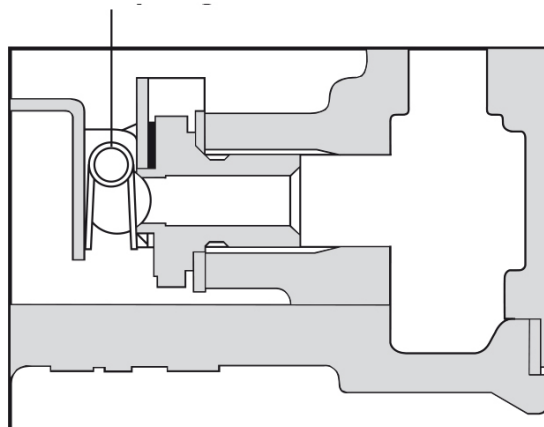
Coupe de l'ensemble clapet principal - 1" (DN25) uniquement
